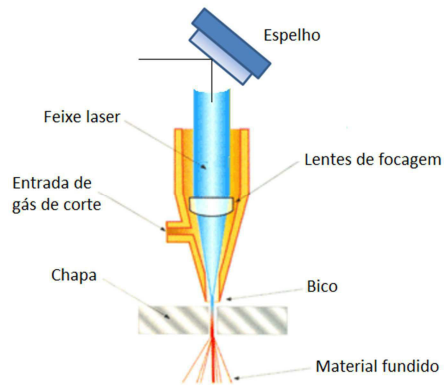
Princípio do corte por laser [FONTE: adaptado [55] e [56]].
